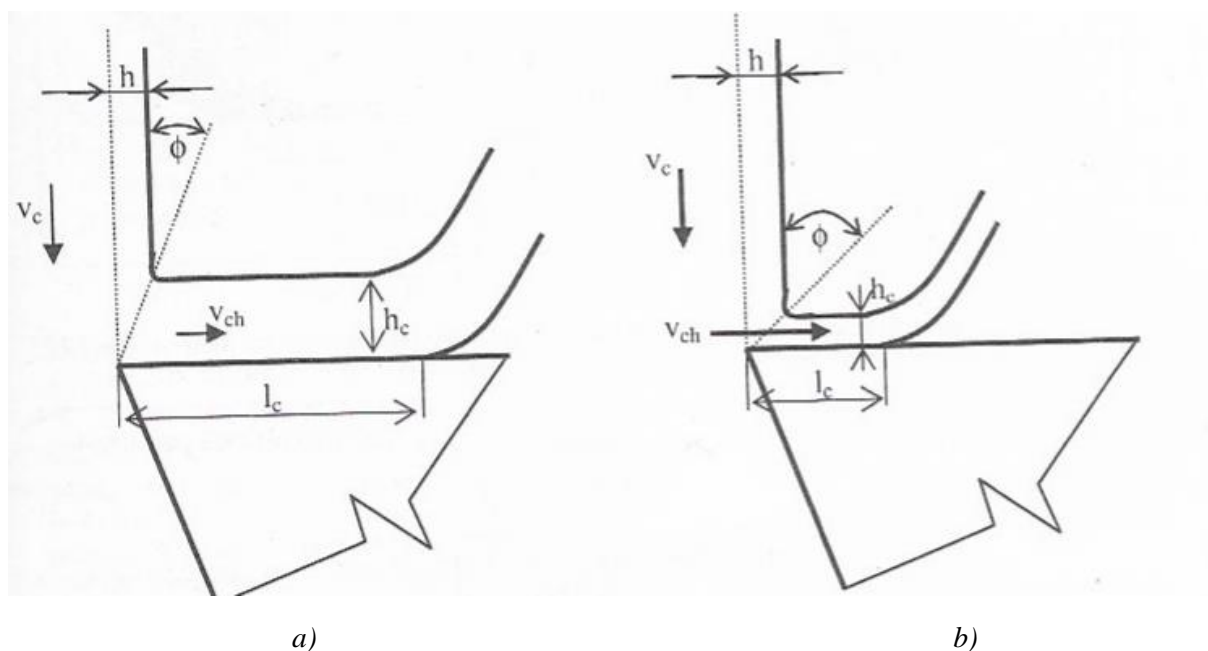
Některé rozdíly mezi soustružením před a po tepelném zpracování, podle [19].
